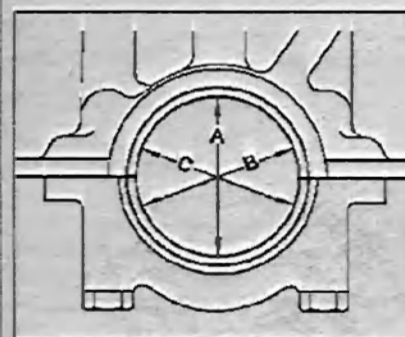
а. Направления для измерения диаметра отверстия под коренной подшипник коленчатого вала.
